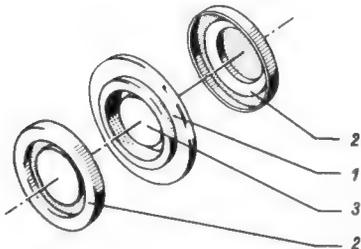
Bestandteile der Siemens-Silizium-Gleichrichterzelle mit Druckkontakt; 1 = Keramikring, 2 = Membranen, 3 = Siliziumtablette
